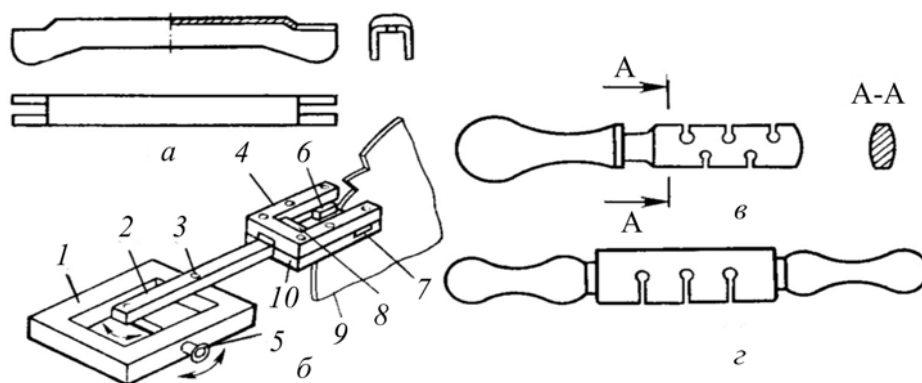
Вспомогательные приспособления для фуговки и разводки зубьев: *а* – фуганок для пильных цепей ПЦУ; *б* – фуговальное приспособление для круглых пил: 1 – рамка; 2 – рычаг; 3 – ось вращения рычага; 4 – вилка для крепления брусков; 5 – винт для поворота рычага; 6, 7 – боковые фуговальные бруски; 8 – центральный фуговальный брусок; 9 – пильный диск; 10 – планка зажима брусков; *в*, *г* – разводки
